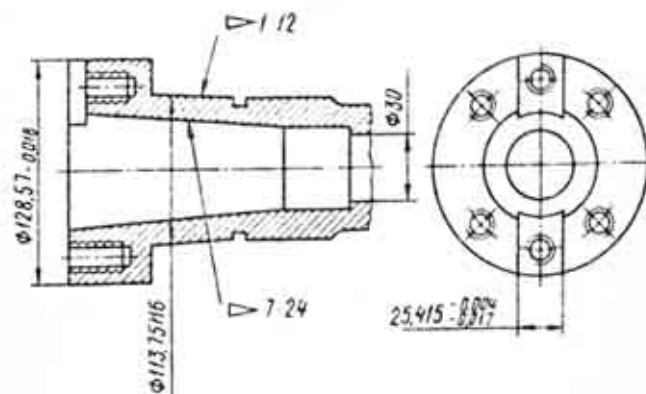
Посадочные и присоединительные размеры конца шпинделя
